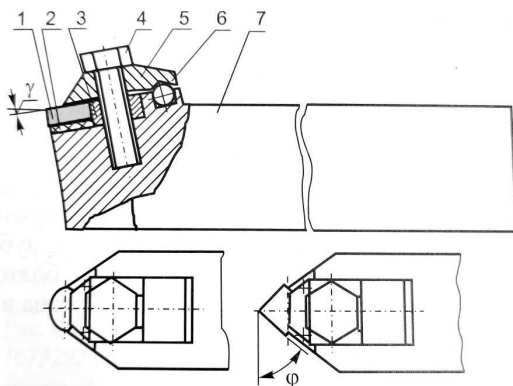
Стандартна конструкція різця з НТМ для обробки загартованих сталей: 1 – різальна пластина; 2 – опорна пластина; 3 – сепаратор; 4 – болт; 5 – прихват; 6 – куля; 7 – державка
